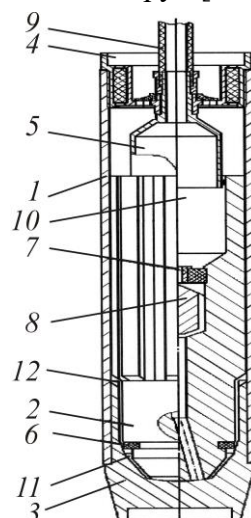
Схема пневмомолота с упругим и инерционным клапанами в системе воздухораспределения: 1 — корпус; 2 — ударник; 3 — наковальня; 4 — хвостовик; 5 — патрубок; 6 — упругий клапан (резинное кольцо); 7 — жиклер; 8 — инерционный клапан; 9 — рукав; 10 — камера прямого хода; 11 — камера обратного хода; 12 — пазы
